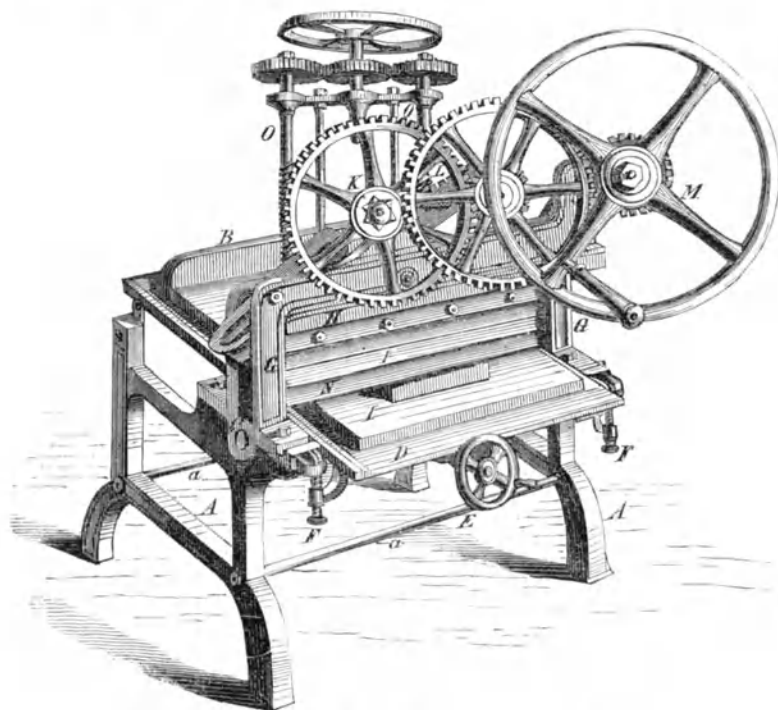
Gebr. Heim's Papierbeschneidemaschine.
